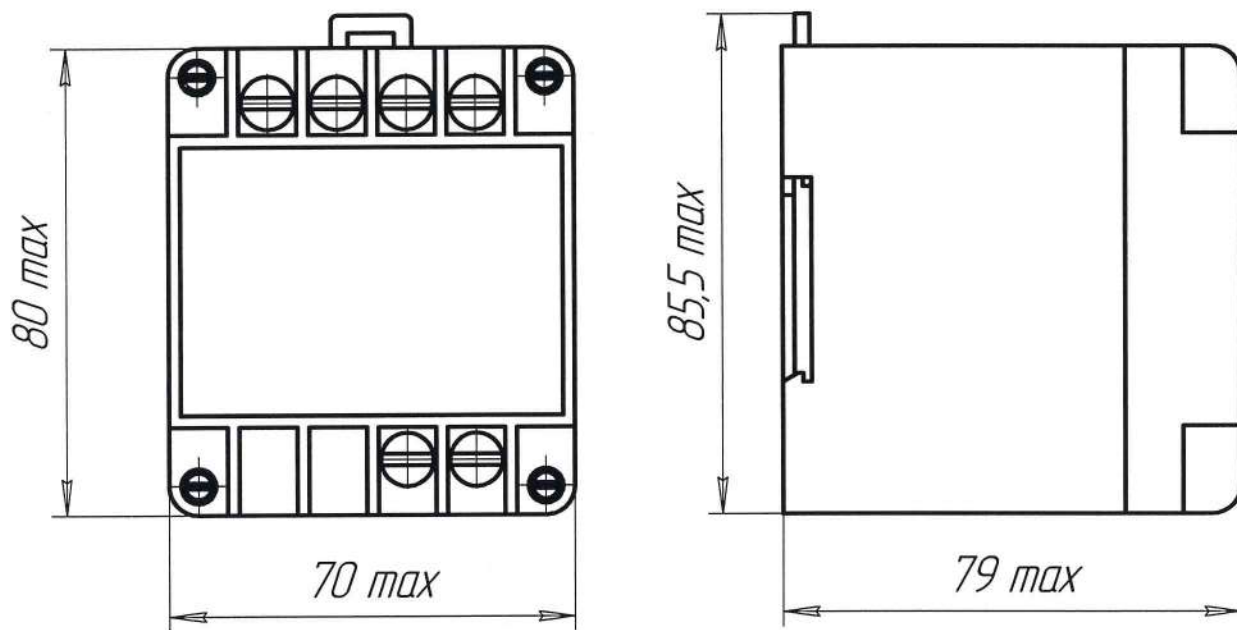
Габаритные, установочные размеры преобразователей переменного тока и напряжения ЕПЗ4Д
